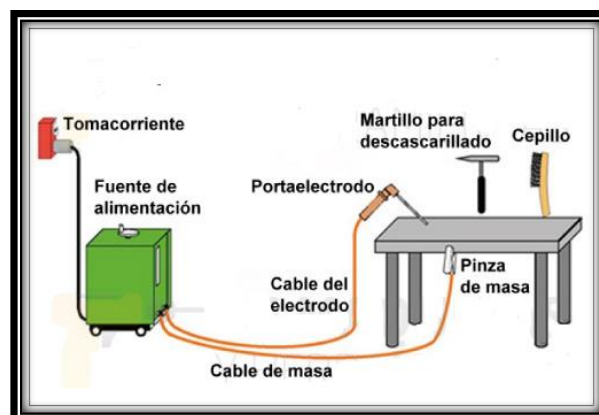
Proceso de soldadura por arco con electrodo revestido
